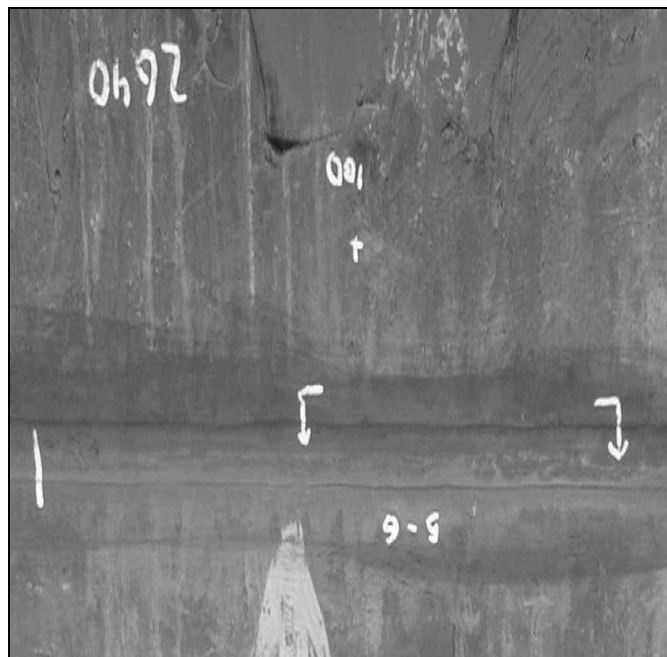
Вид поверхности дефекта катушки №2640: знаком ... обозначено намеченное место ремонта сваркой
